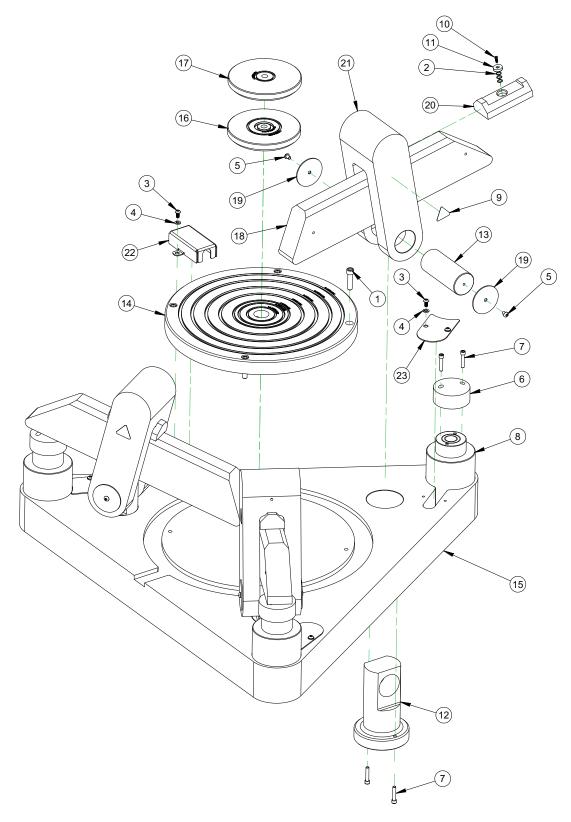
Рабочая поверхность стола в сборе (№ части 88408)
